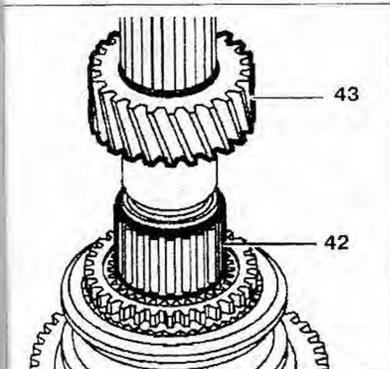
Снимите игольчатый подшипник 42 и шестерню 43 5-й передачи.
